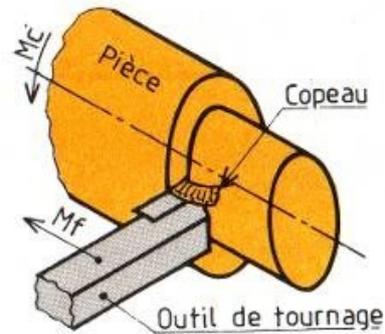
Mouvements de coupe et d'avance en tournage.
